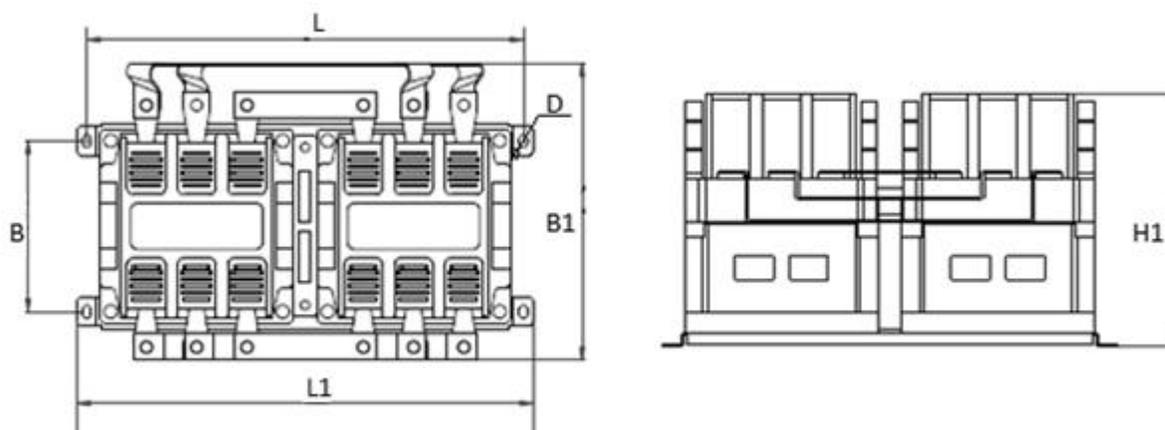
Пускатель реверсивный типа ПМ12 315-630А. Степень защиты - IP00
